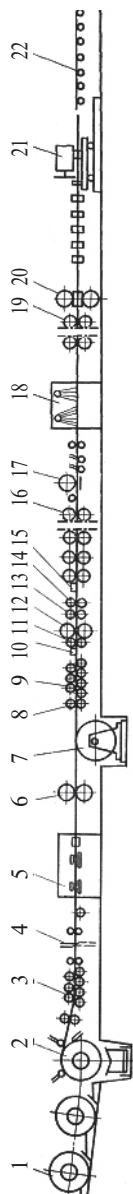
Стан для производства гнутых сварных профилей: 1 — загрузочная площадка; 2 — разматыватель; 3 — правильная машина; 4 — ножницы с верхним резом; 5 — стыкосварочная машина с гратосни-мателем; 6 — задающие ролики; 7 — моталка-накопитель; 8 — задающие ролики правильной машины; 9 — правильная машина; 10 — дисковые ножицы для подрезки кромок; 11 — вводной направляющий стол; 12 — задающие ролики; 13 — тянущие ролики; 14 — кромкокрошитель для обрезанной кромки; 15 — приемный стол профилигоночного агрегата; 16 — профилигоночный агрегат; 17 — сварочная машина; 18 — система охлаждения сварного шва; 19 — калибровочные валки; 20 — отводной рольганг; 21 — дисковая пила; 22 — отводной рольганг
